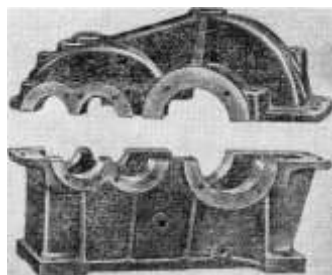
Литые корпус и крышка двухступенчатого цилиндрического редуктора с разъемом по осям валов
